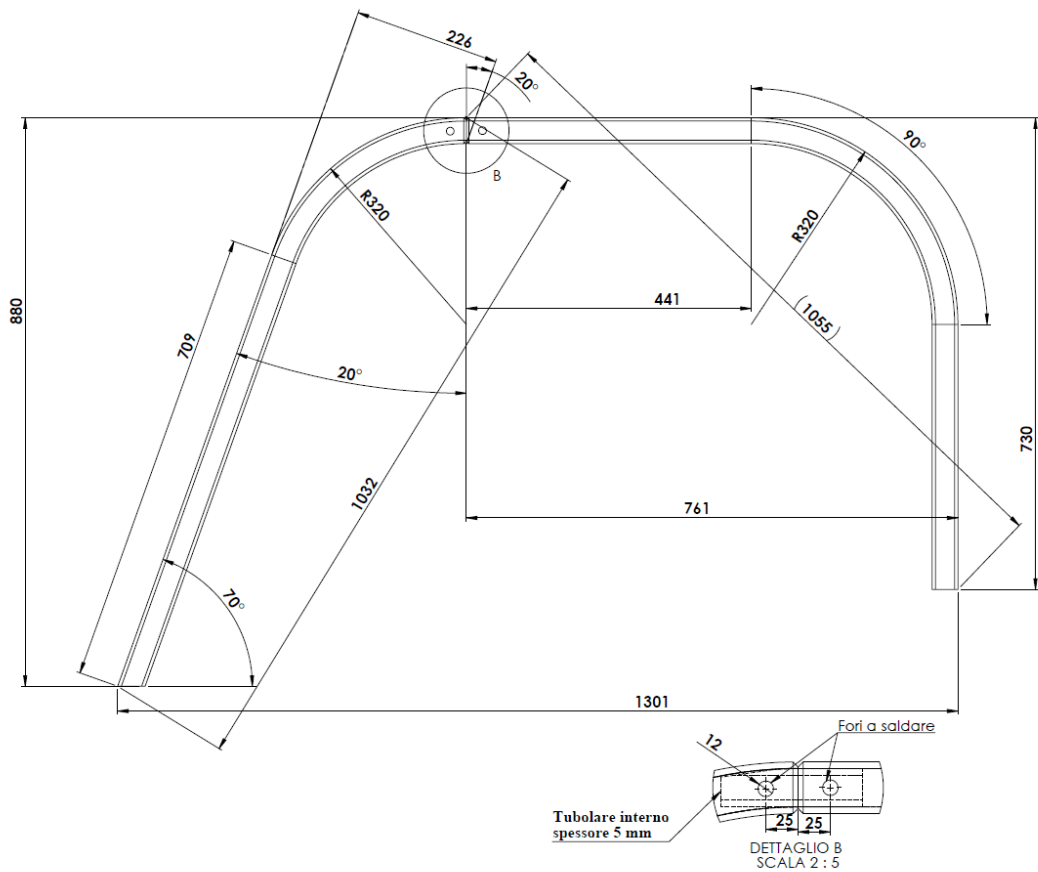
Profilo laterale del telaio di protezione, dettagli costruttivi e giunto a innesto saldato.
